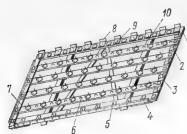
1 — основание; 2 — покрытие; 3 — упорная планка-линейка; 4 — стойка; 5 — ручка прижима; 6 — держатель; 7 ручка; 8 — направляющая; 9 пружина возвратная прижима; 10 — плитка
